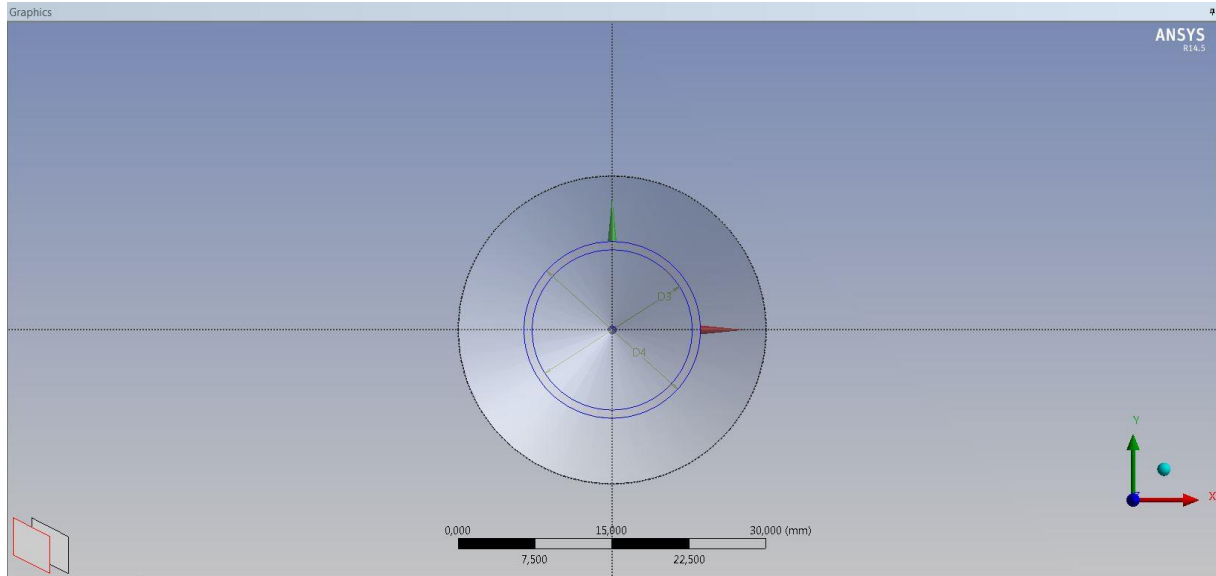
Dimensão da espessura do tubo e do furo de entrada.
